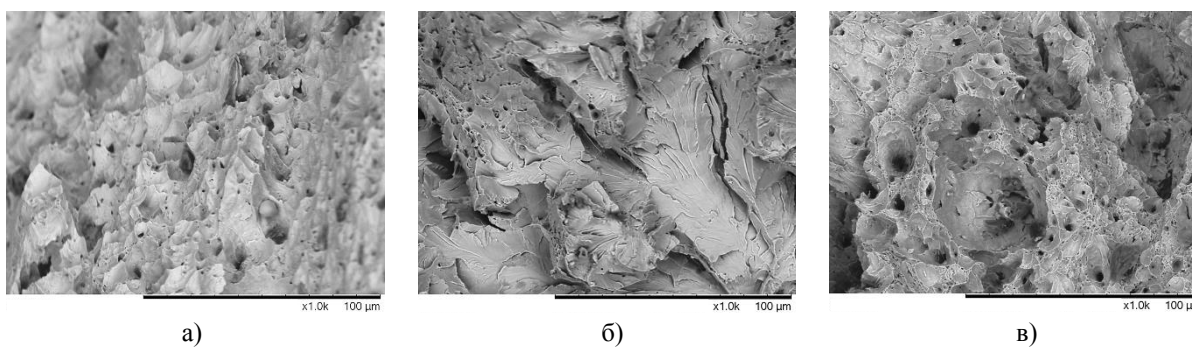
Микрорельефы изломов (разрушения) образцов: а - образца из стали 09Г2С в состоянии поставки; б - сварного образца из 09Г2С, подвергнутого РКУП ($C, n=2, T=823$ К), в ЗТВ; в - сварного образца из 09Г2С после закалки (в воде от 1203 К) и РКУП ($C, n=2, T=823$ К) в ЗТВ, подвергнутых ударному изгибу при 233 К
